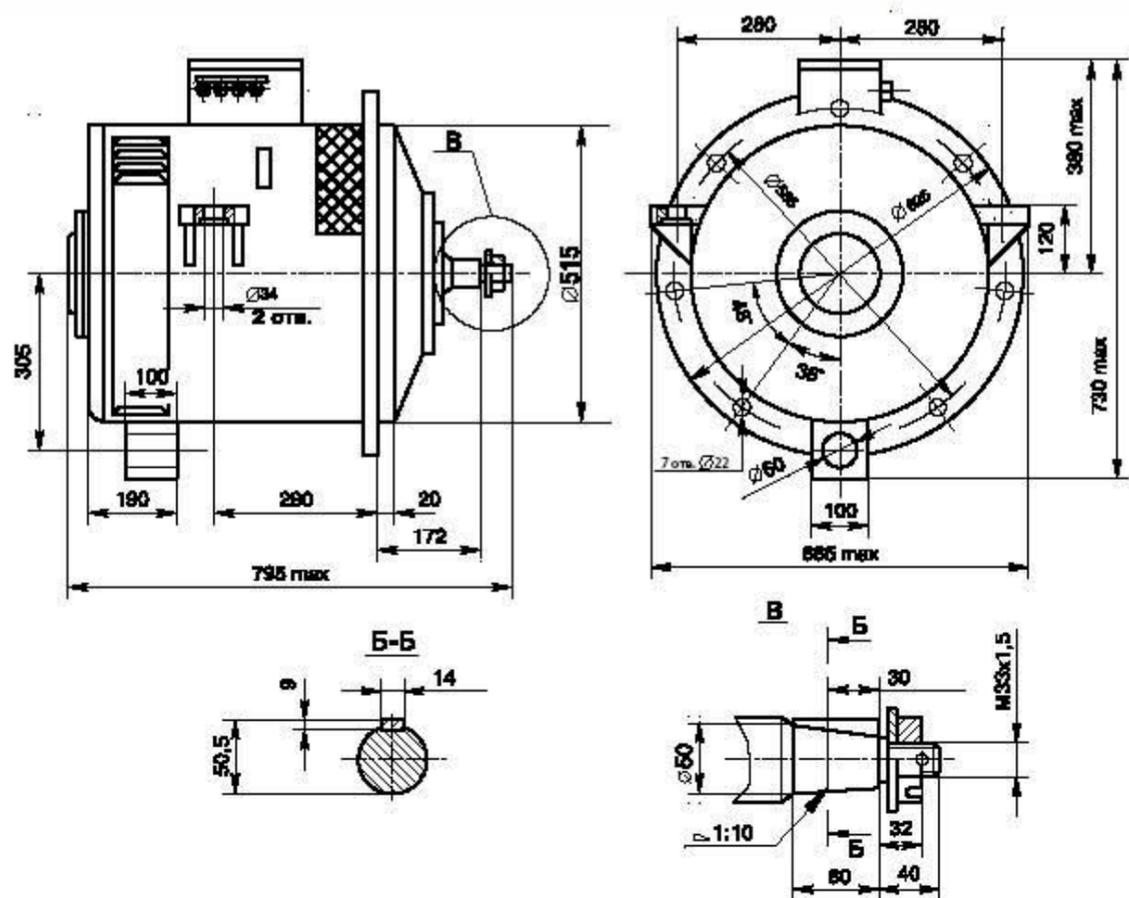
Габаритные и установочные размеры электродвигателя ДТН-46/33М
